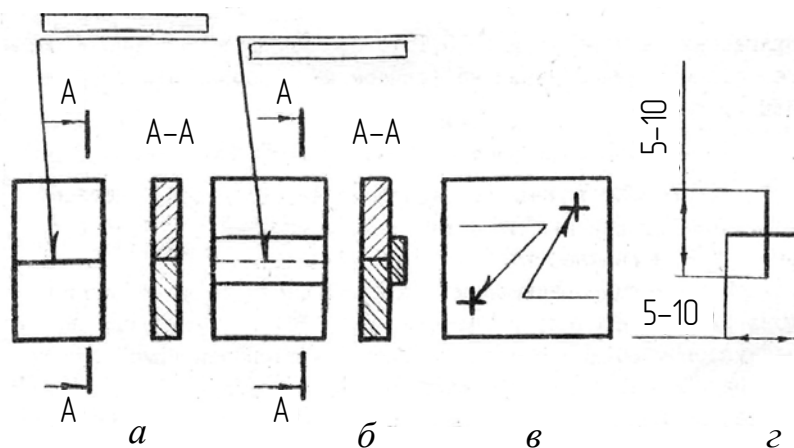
Изображение стандартных швов сварных соединений
